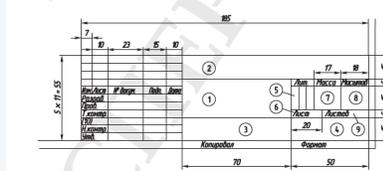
Пример заполнения граф. основной надписи: 1 — наименование изделия; 2 — обозначение документа; 3 — обозначение материала детали по стандарту; 4 — сведения об изготовителе чертежа; 5 — литера документа; 6 — порядковый номер листа; 7 — масса изделия в килограммах; 8 — масштаб; 9 — общее количество листов документа
